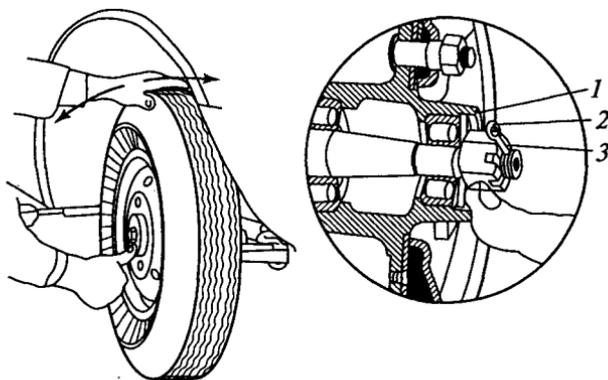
Проверка люфта в подшипниках ступицы колеса:
